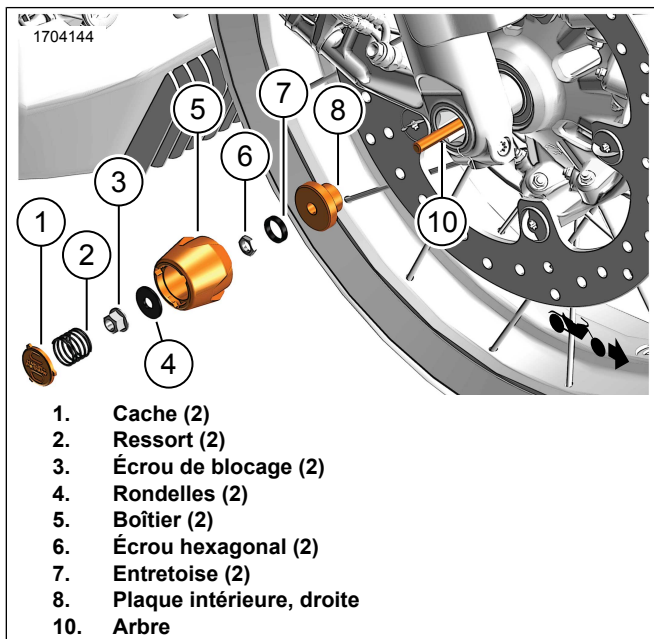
Ensemble de couvercle d'essieu avant (côté droit illustré)
